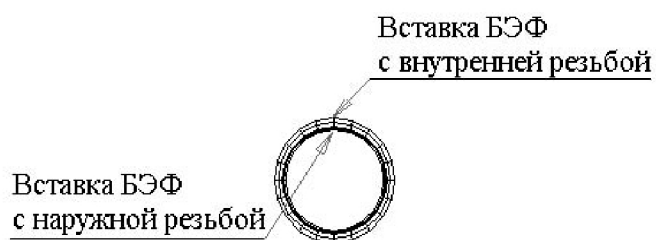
Определение диаметра сопрягаемой поверхности резьбового БЭФ
